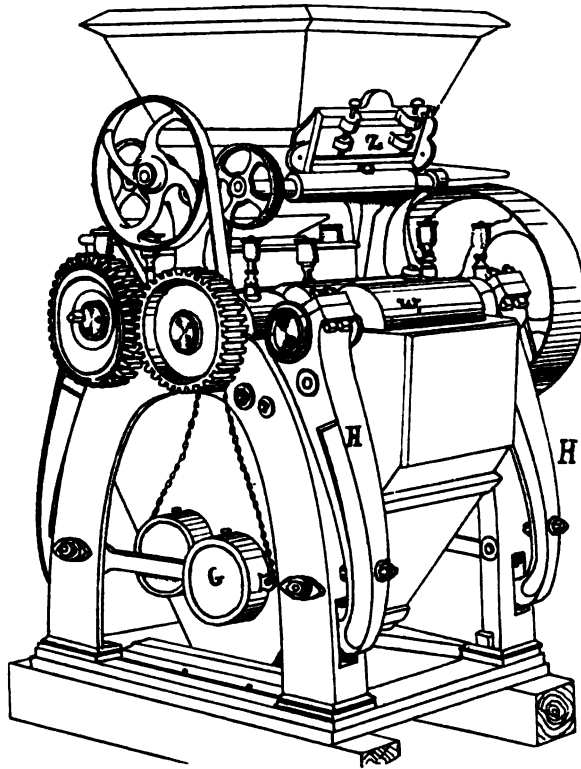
Walzenstuhl mit zwei Walzenpaaren.
